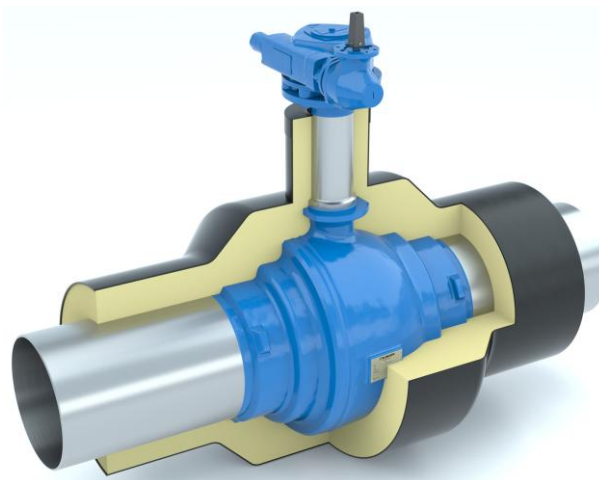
Kugelhahn für die Erdverlegung (vorisoliert) mit Volldurchgang, doppelter Lagerung, Handgetriebe und Schweissenden. Quelle: Klinger Gysi, KHSVI-VVS DN 150-250
